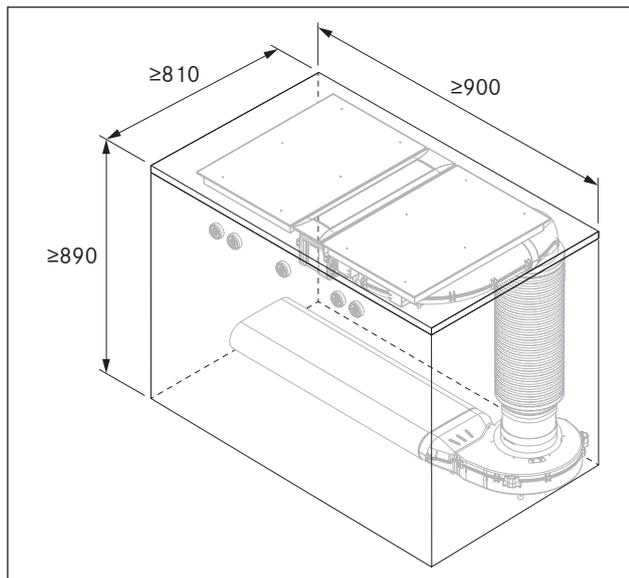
Dimensioni minime di montaggio PKA3/PKA3AB per il montaggio standard
